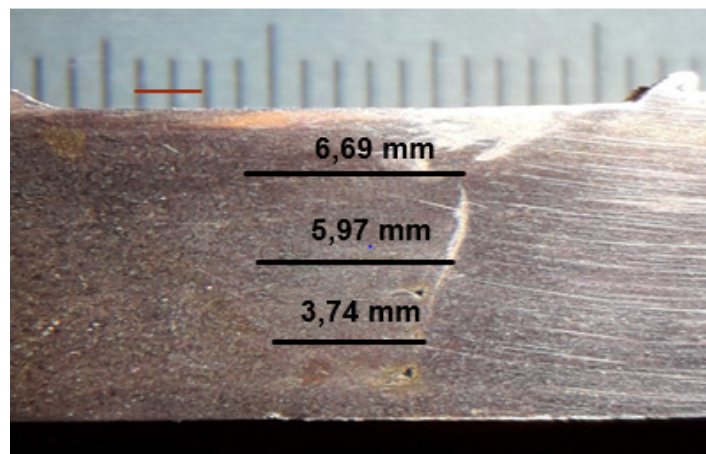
Perfil transversal cordones de soldadura
